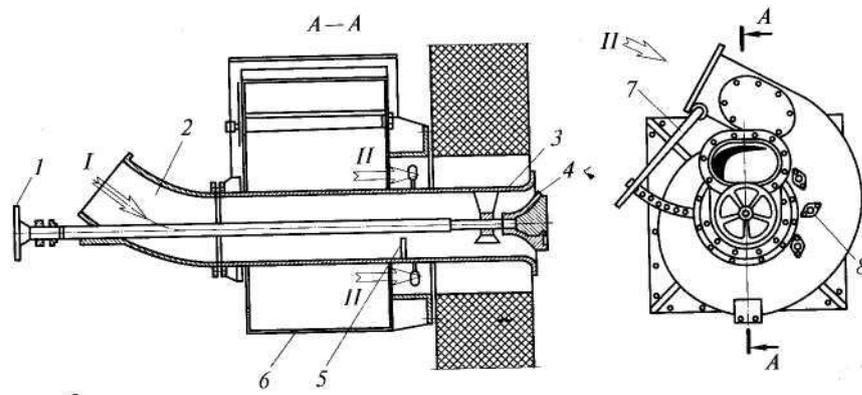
Вихревая пылеугольная горелка ОРГРЭС: 1 – штурвал управления конусом; 2 – входной патрубок первичного воздуха; 3 – наконечник; 4 – конус-рассекатель; 5 – порог; 6 – улитка вторичного воздуха; 7 – рукоятка языкового шибера; 8 – отверстие для мазутной форсунки; I, II – потоки первичного и вторичного воздуха.
